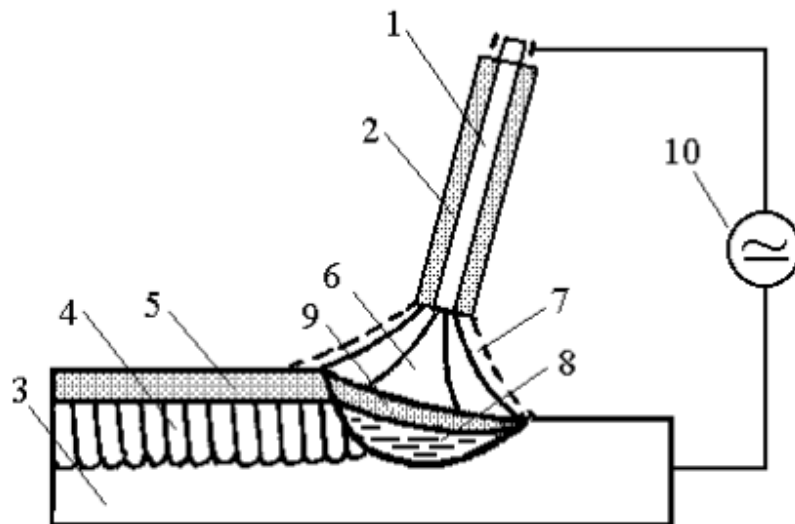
Схема ручного дугового зварювання покривним електродом
